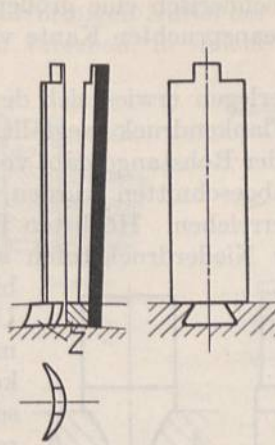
Schaufelbefestigung mittels Schwalbenschwanzes.
